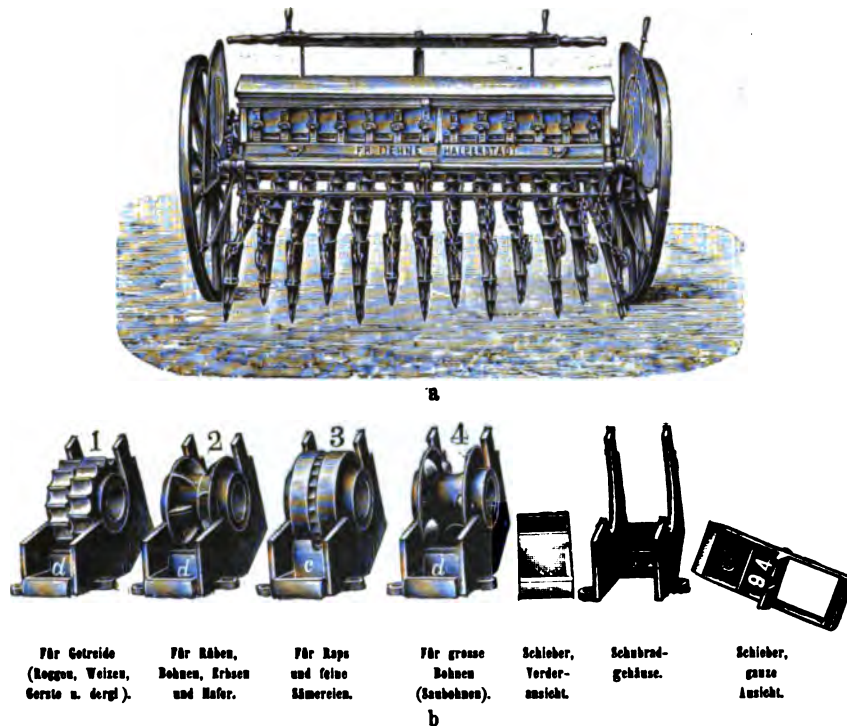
a Drillmaschine mit Schubradsystem von Fr. Dehne-Halberstadt, b die verschiedenen Schubräder zu dieser Drillmaschine.
